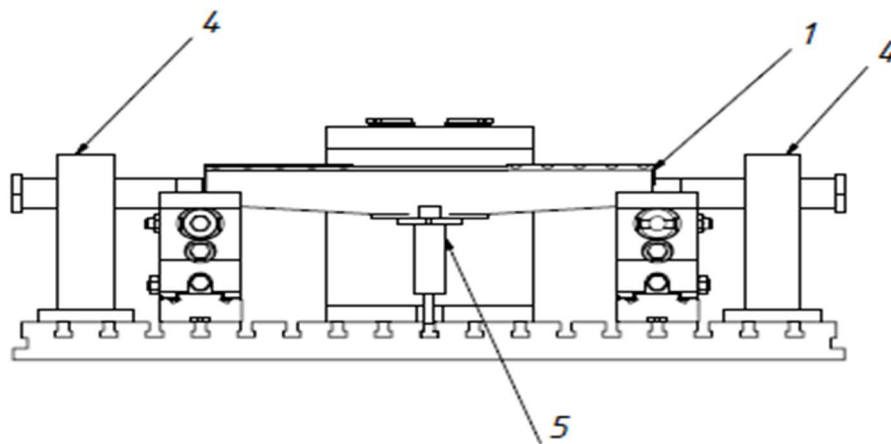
Свердлильний пристрій (Вид 1)
